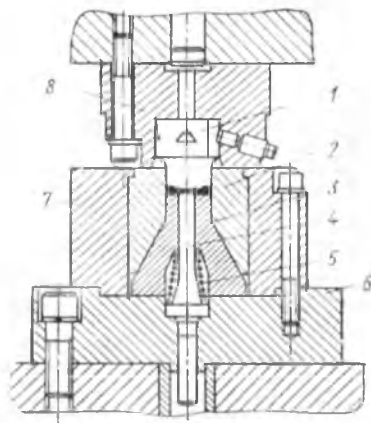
Штамп для высокоскоростной штамповки поковки дисковой фрезы:
